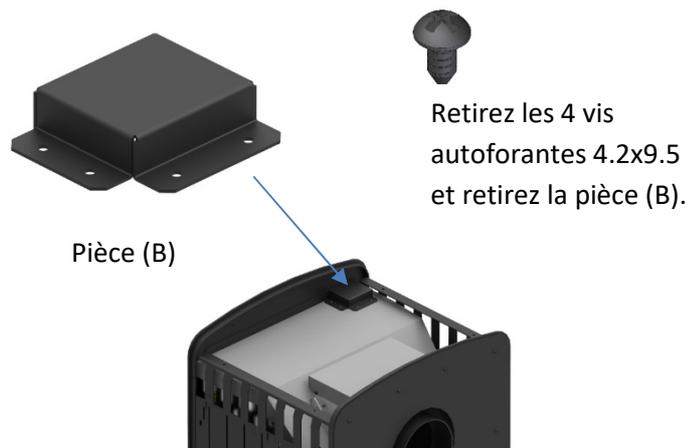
Retirer la pièce (B) de l'équipement Natura Cream ou Natura Black
